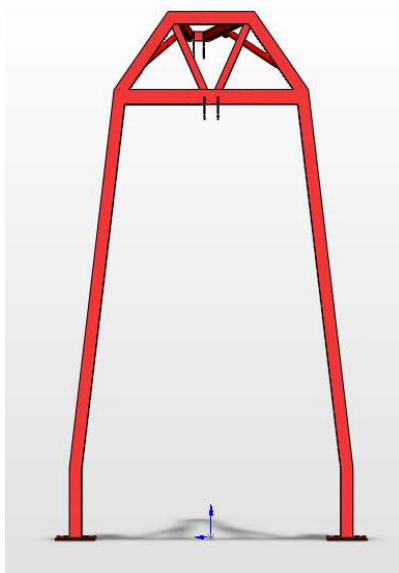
Vista frontal da estrutura de suporte elevada.
